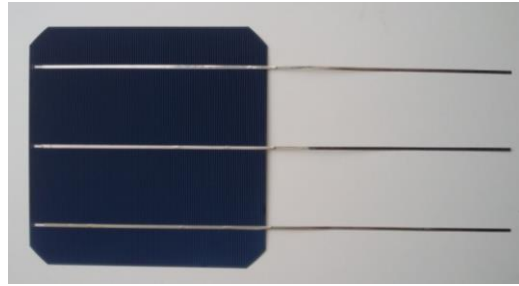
Celda soldada con conductores Tab Wire
